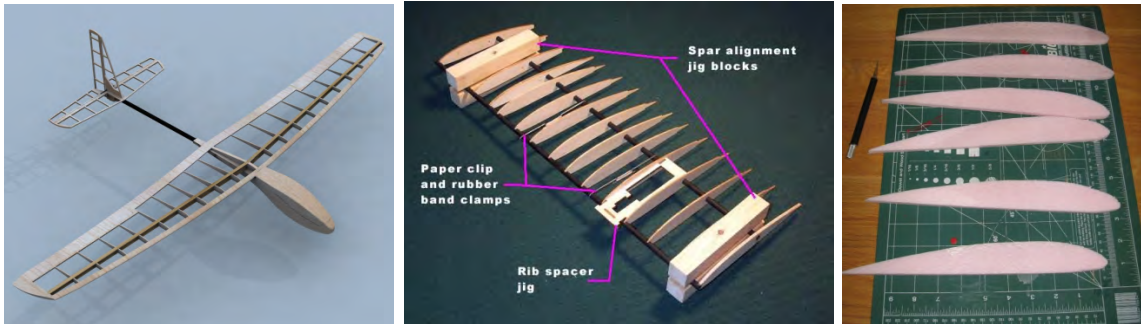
Planeador, andamiaje de fabricación, plantillas de perfil
